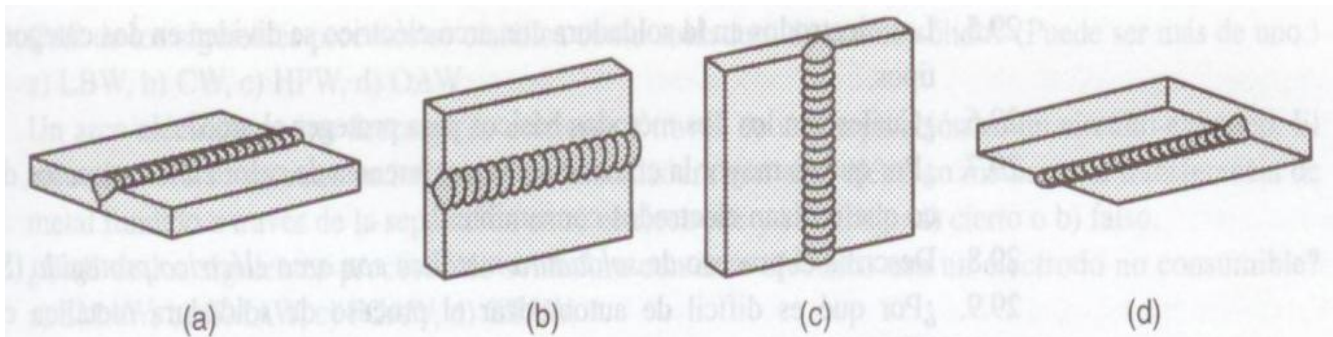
Posiciones para soldadura (definidas aquí para soldaduras en ranuras): (a) plana, (b) horizontal, (c) vertical y (d) sobre cabeza.
